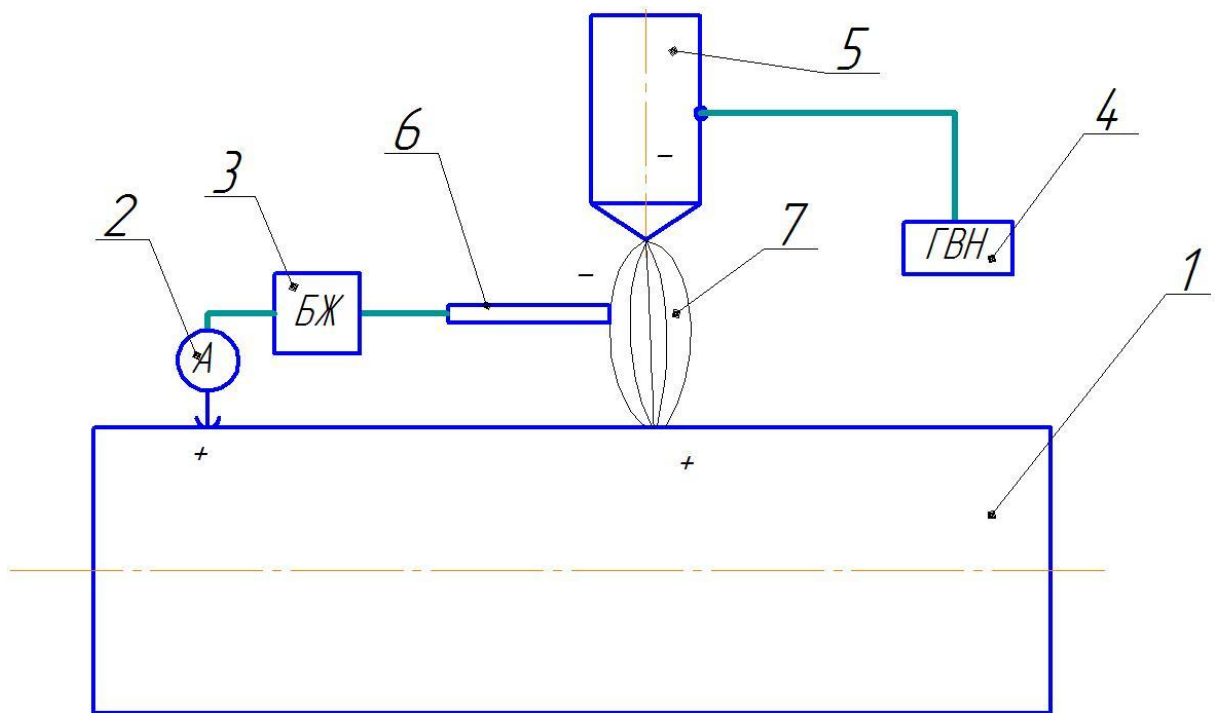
Схема місцевого зміцнення сталевих деталей: 1 – деталь; 2 – електричний струм; 3 – блок живлення; 4 – генератор високої напруги; 5 – електрод коронного розряду; 6 – робочий електрод; 7 – коронний розряд
